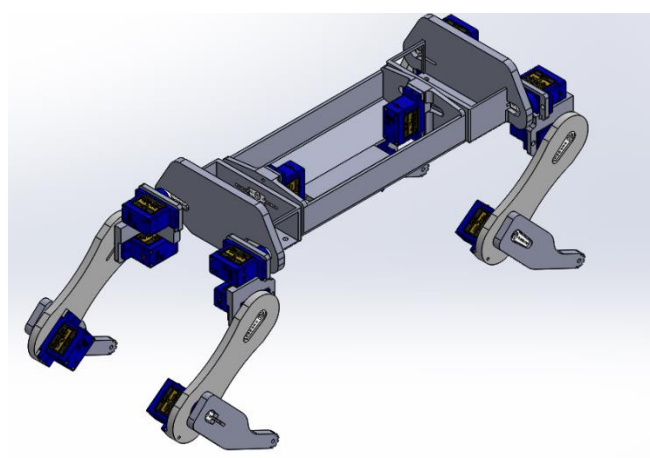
Diseño CAD Vista Isométrica [Elaboracion propia]
